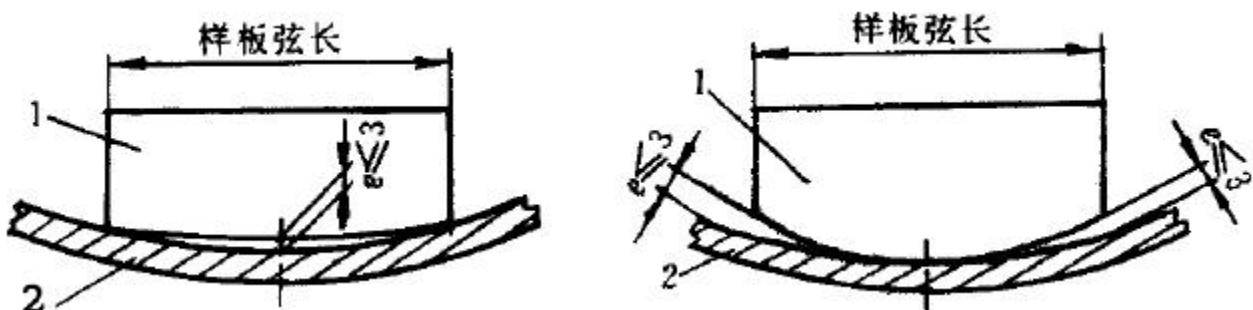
球壳板曲率检查 (单位: mm)
